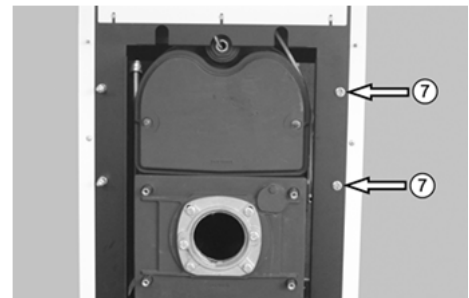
Mit Sechskantschrauben befestigtes Halteblech
